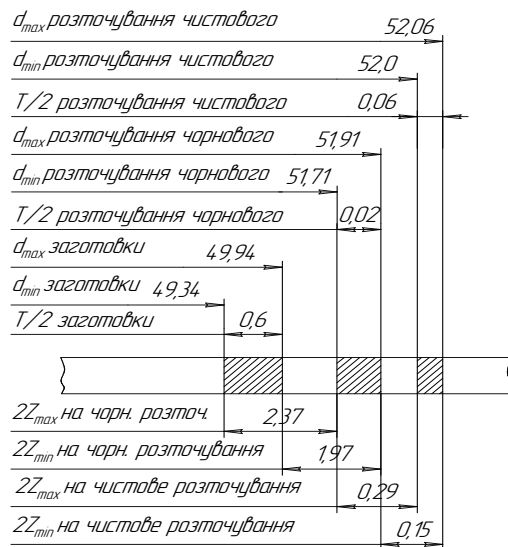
Схема розташування припусків та допусків на оброблення отвору корпусу підшипника.
